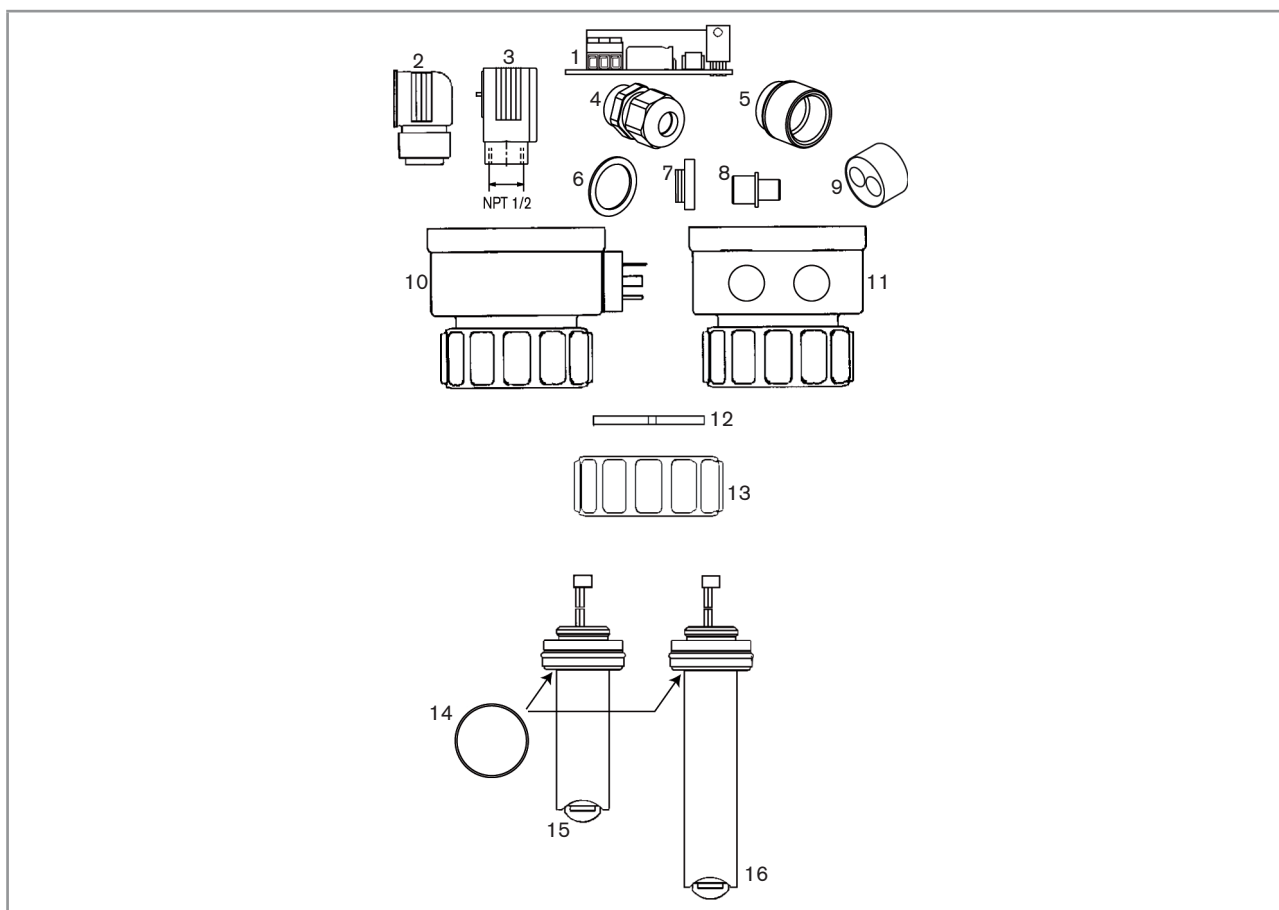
Explosionszeichnung der Ersatzteile, 8025 in Kompakt-Ausführung
